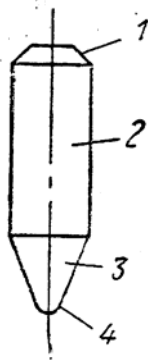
Керн: 1 – фаска; 2 – циліндрична частина; 3 – конічна частина; 4 – сферична частина (робоча поверхня).
